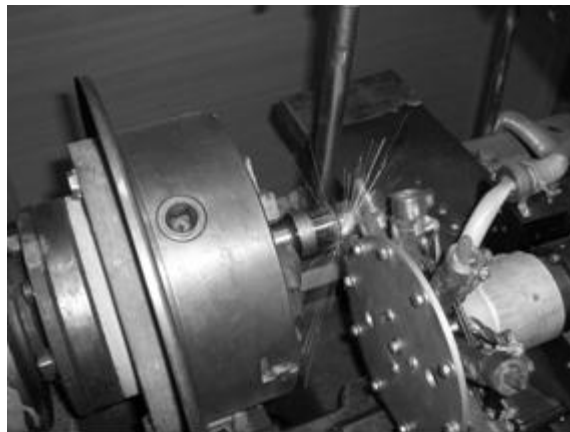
Процесс нанесения твердого сплава на поверхность оправки
